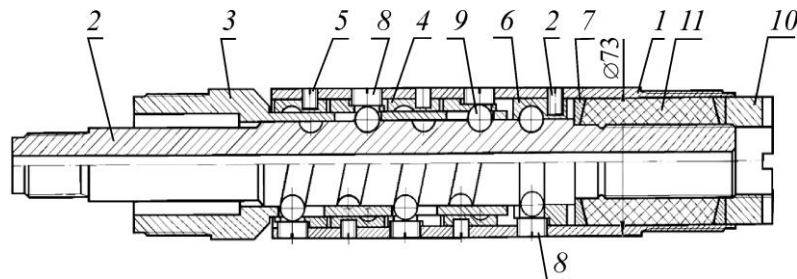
Синусошариковый редуктор в устройстве для развинчивания труб в скважине: 1 — корпус; 2 — ведущий вал; 3 — водило; 4 — охватывающие втулки; 5 — винты; 6 — обойма подшипников; 7 — кольца; 8 — пробки для ввода шариков; 9 — шариковые сателлиты; 10 — гайка; 11 — пеньковое сальниковое уплотнение
